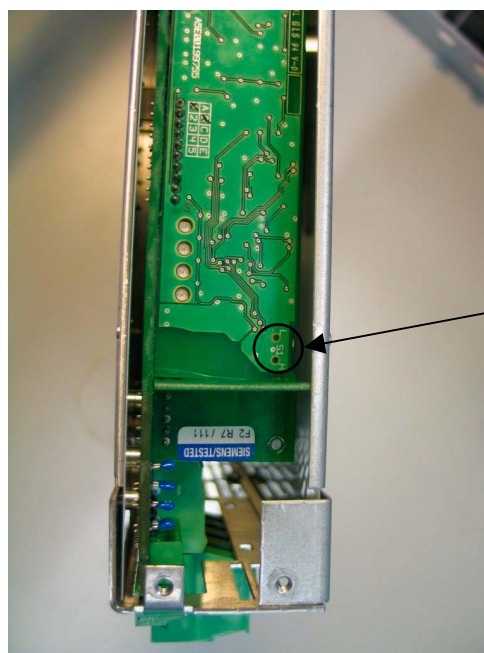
Schalter S1 für Ansprechschwelle Bremsen 5 – 50 kW
